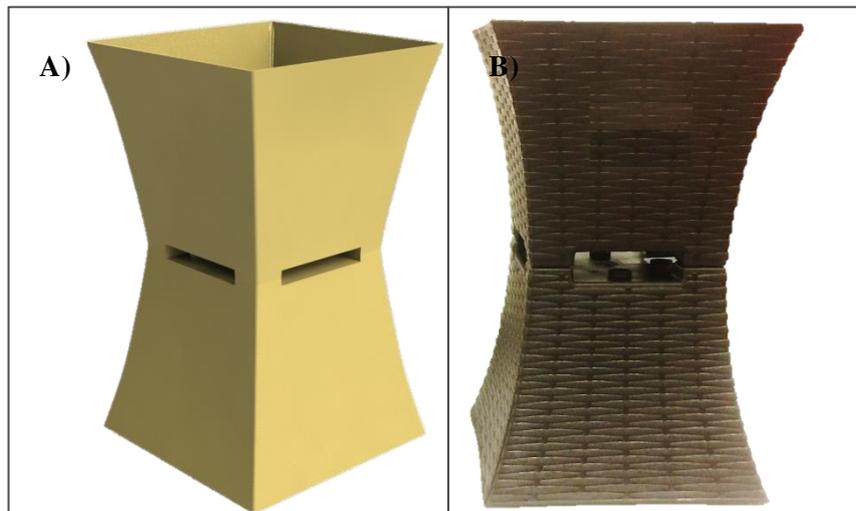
GEOMETRÍA ESTRUCTURA EXTERNA: A) DISEÑO CAD, B) DISEÑO CON PIEZA COMERCIAL
